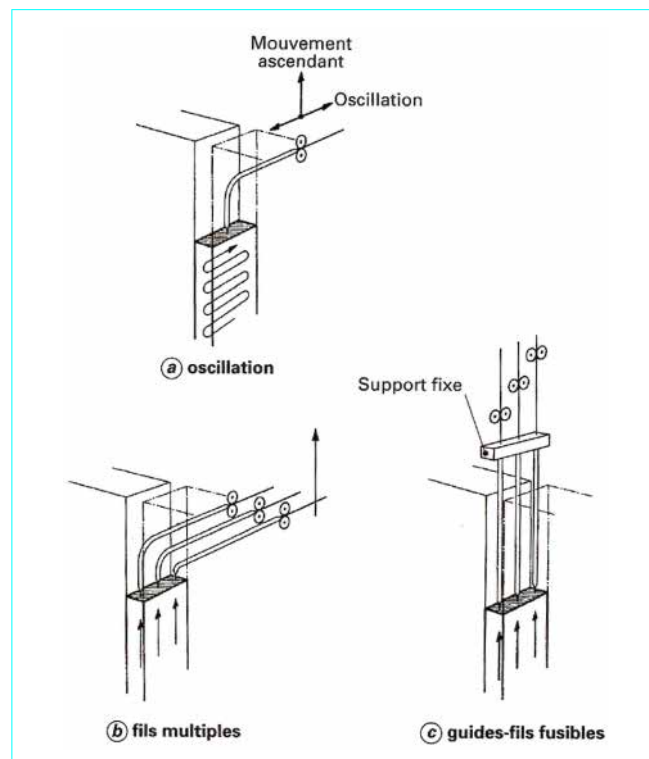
Variantes de soudage vertical sous laitier
